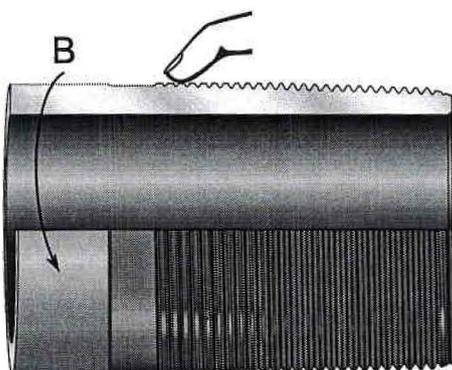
Проверка неровностей и шероховатости ниток неполного профиля резьбы и заходной фаски.
